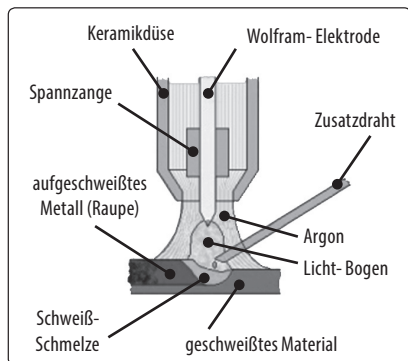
, Prinzip der TIG-Methode mit Einsatz vom Schweißstab
